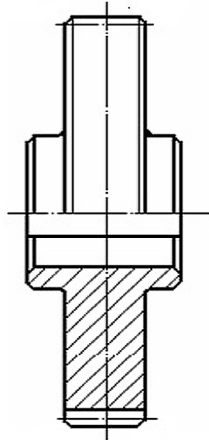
Зубчатое колесо с симметричной ступицей
